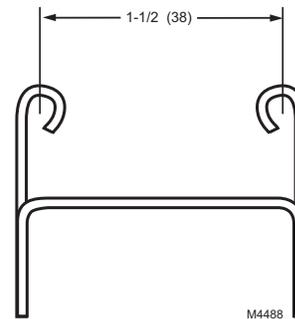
Sujetador de montaje del sensor para exteriores C7089U1006. Dimensiones en pulgadas (mm).
